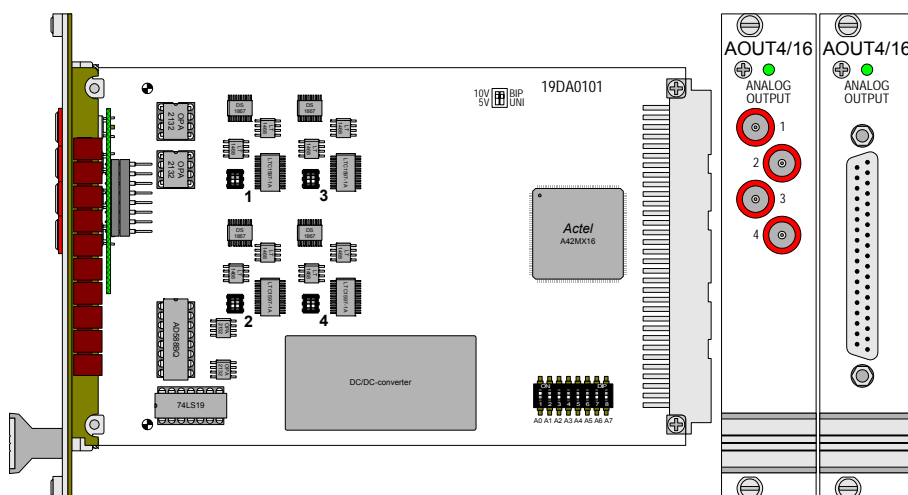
Pro-AOut-4/16 REVB: Platine und Frontplatte
